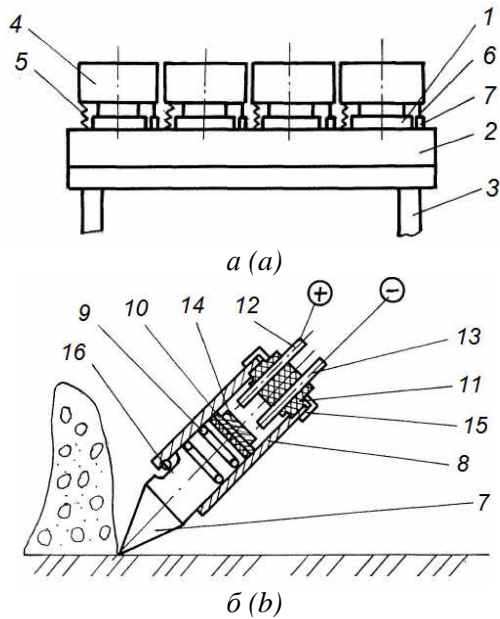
Бульдозерне устаткування з активними різальні елементами: *а* – бульдозерний відвал; *б* – конструкція розпушувального зуба; 1 – активний зуб; 2 – траверса; 3 – тяга; 4 – ріжучий елемент; 5 – пружина; 6 – штовхач; 7 – буфер; 8 – циліндричний корпус; 9 – ущільнювач; 10 – прокладка; 11 – ізолятор; 12, 13 – електроди; 14 – металева пластина; 15 – накидна гайка; 16 – стопорний штифт
